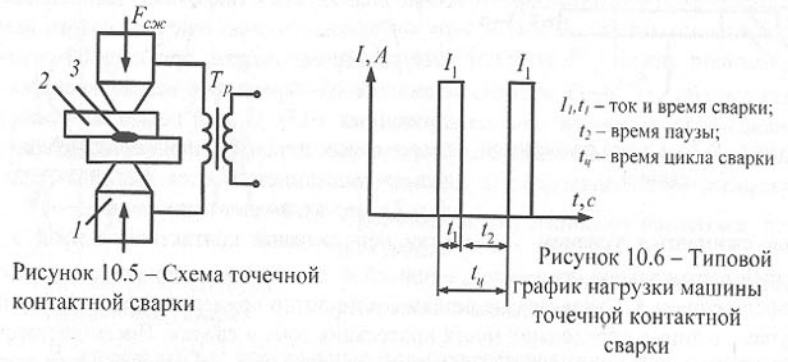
Схема точечной контактной сварки
